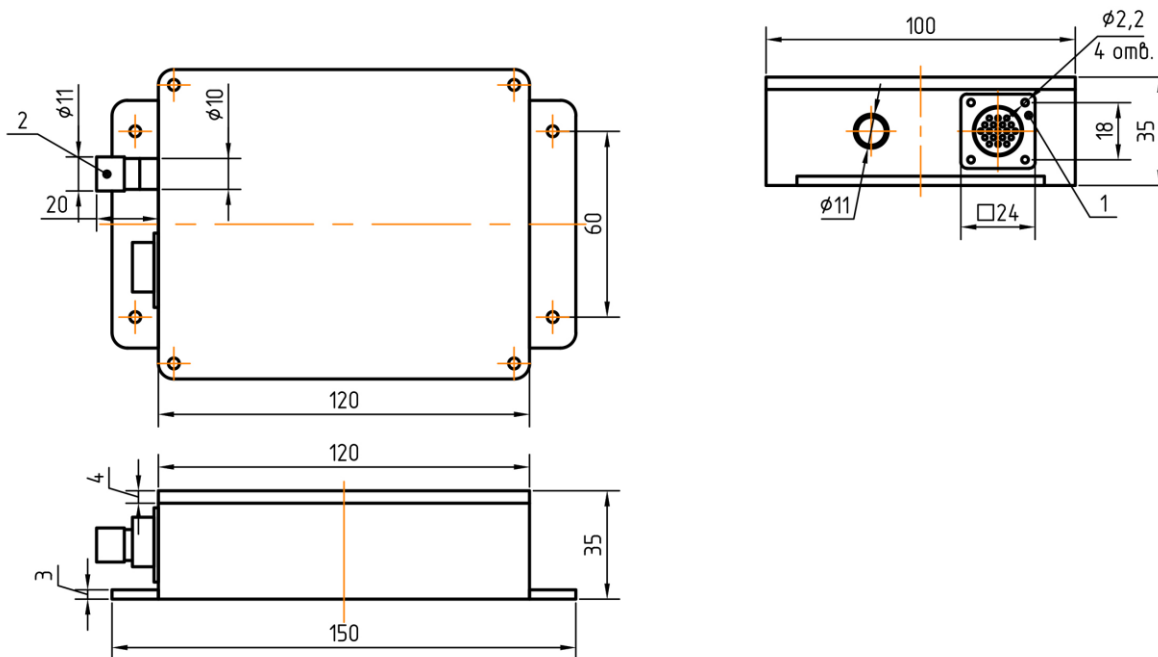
Габаритный чертеж ИИБ ГАЛС-М1АМ
